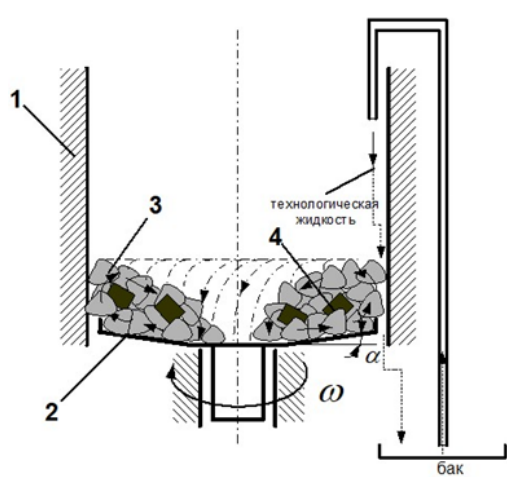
Схема центробежно-ротационной установки: 1 — неподвижная цилиндрическая обечайка; 2 — ротор; 3 — абразивное зерно; 4 — обрабатываемые детали
